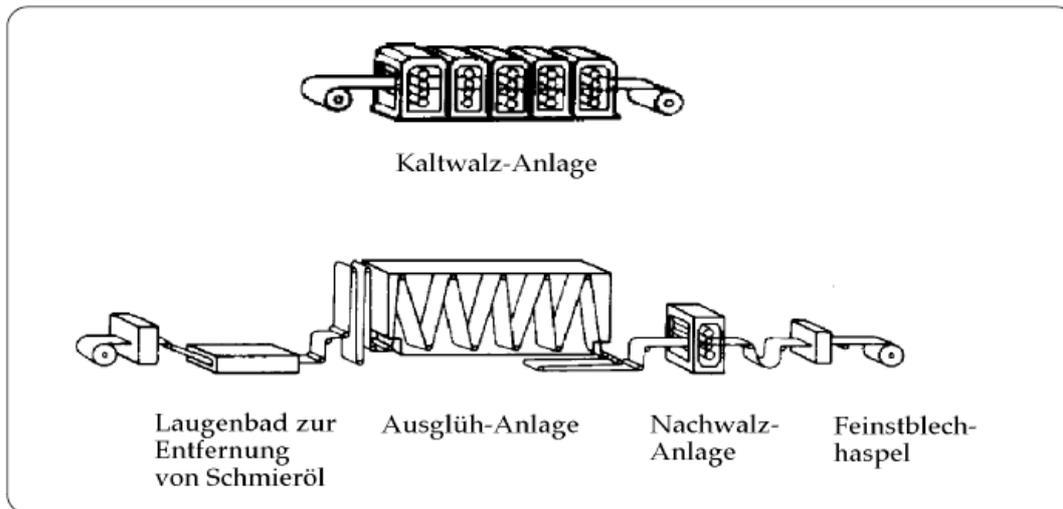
Schema eines Kaltwalzwerks mit anschließender Ausglühanlage ^[11]
